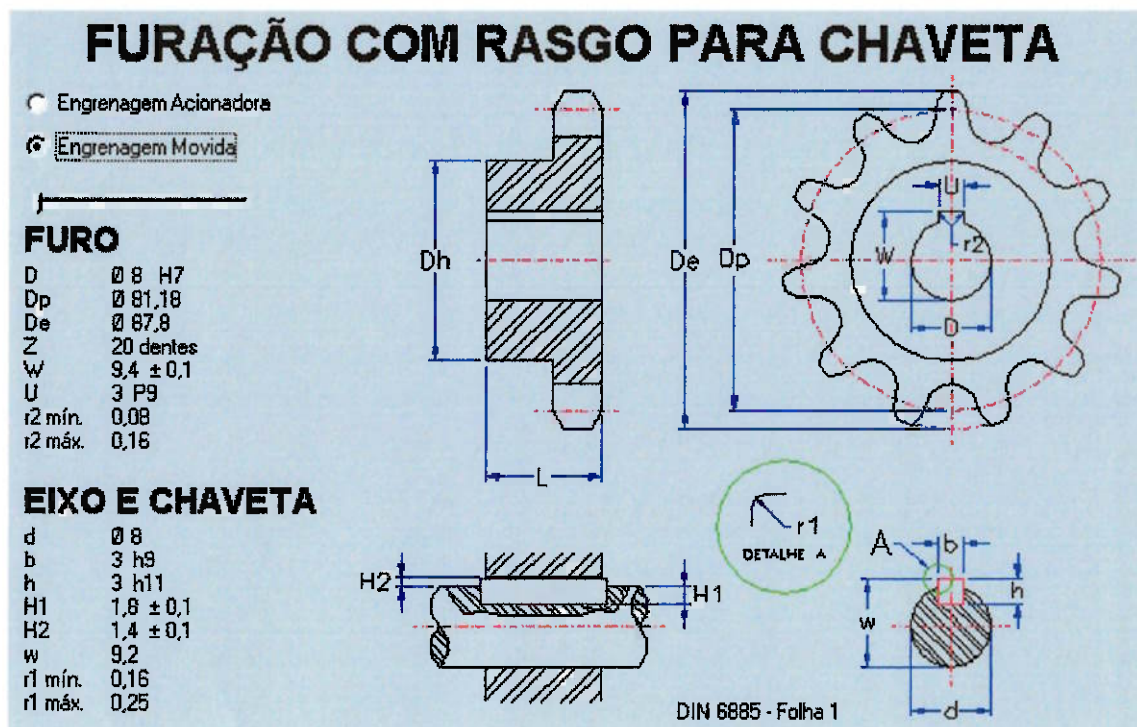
Furação com rasgo para chaveta para engrenagem movida
